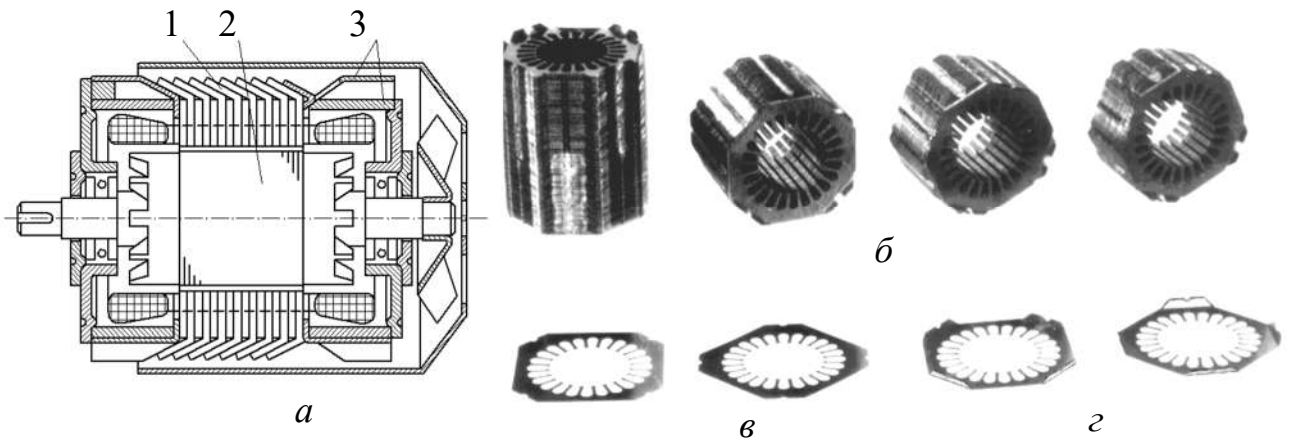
Конструктивна схема закритого безкорпусного асинхронного двигуна (*a*) з магнітопроводом статора (*б*), плоскі заготовки (*в*) і елементарні шари (*г*) електротехнічної сталі просторової структури: 1 – статор; 2 – ротор; 3 – опорно-стяжний елемент.
